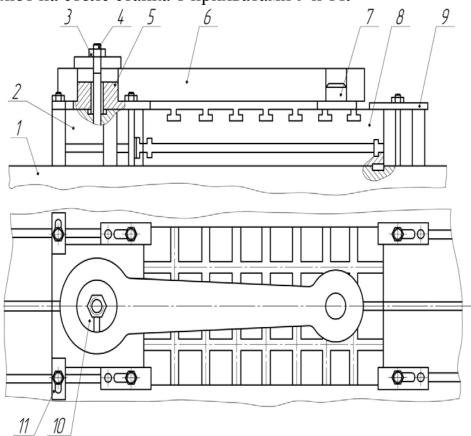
Универсально-сборное приспособление (УСП-ЧПУ) для установки рычага: 1 – стол станка; 2 – гидроцилиндр; 3 – гайка; 4 – шпилька; 5 – втулка; 6 – заготовка; 7 – штырь; 8 – базовая плита; 9, 11 – прихваты; 10 – быстросъемная шайба
